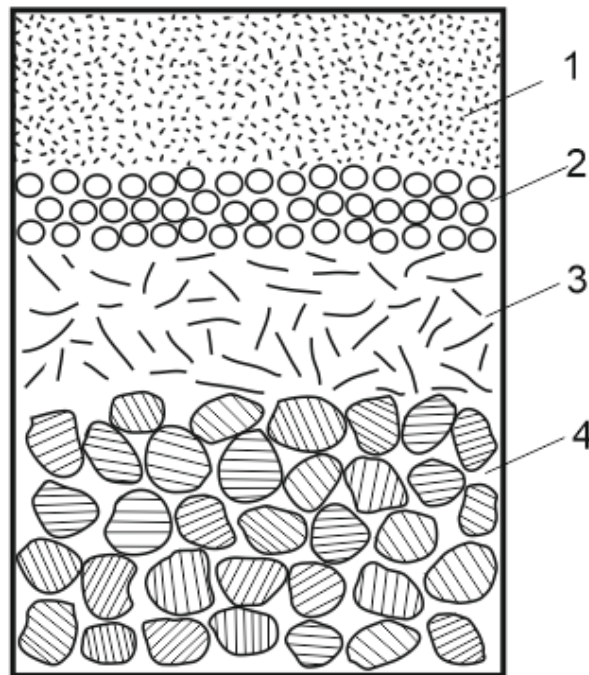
Схема композиційного зміцненого шару при плазмовій обробці після гартування СВЧ: 1 – шар плазмового гартування; 2 – зона відпуску; 3 – шар гартування СВЧ; 4 – вихідний метал
